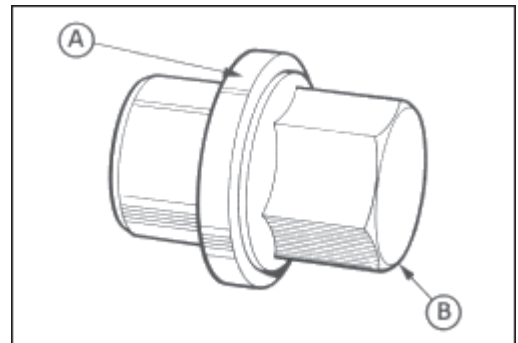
Spez. Befestigungsmutter mit Scheibe
